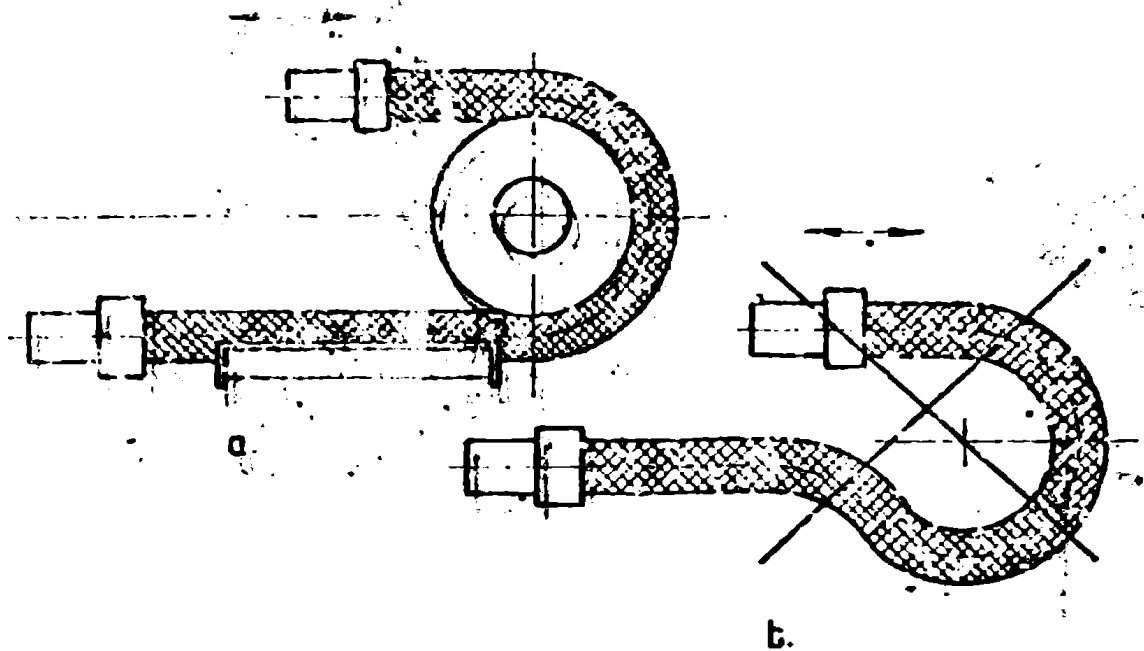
Montaj în arc de 180° cu rolă de sprijin.
